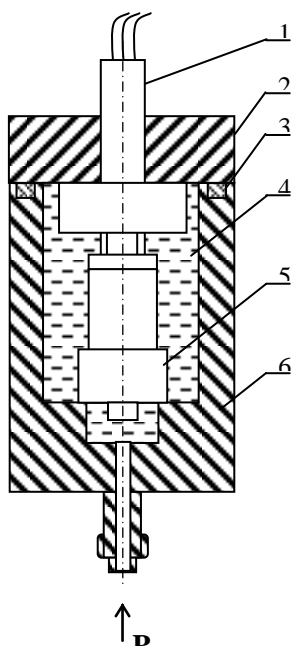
Схема приспособления для испытания тензопреобразователя гидростатическим давлением
